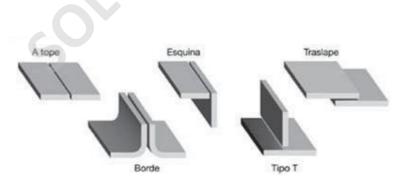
Conexiones de perfiles y planchas por soldadura
